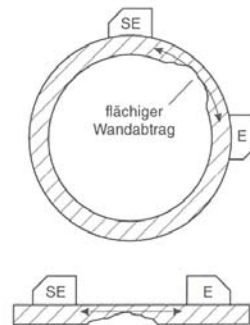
Prüfung auf flächige Korrosion mit geführten SH-Plattenwellen /6-7/
